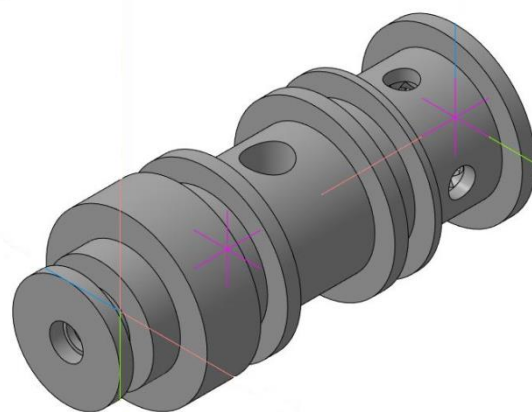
Резьбовая гайка для шаровой. 3D модель
